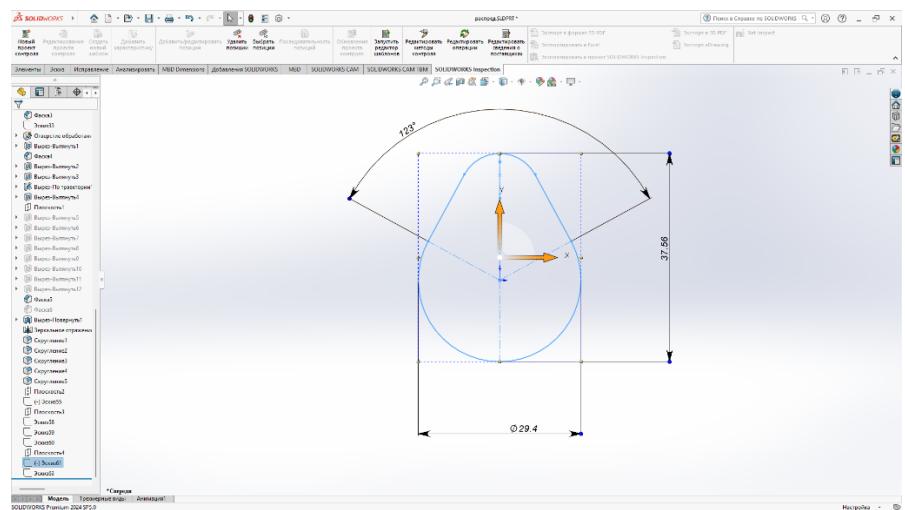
Профиль кулачка впускного клапана Образца 3
